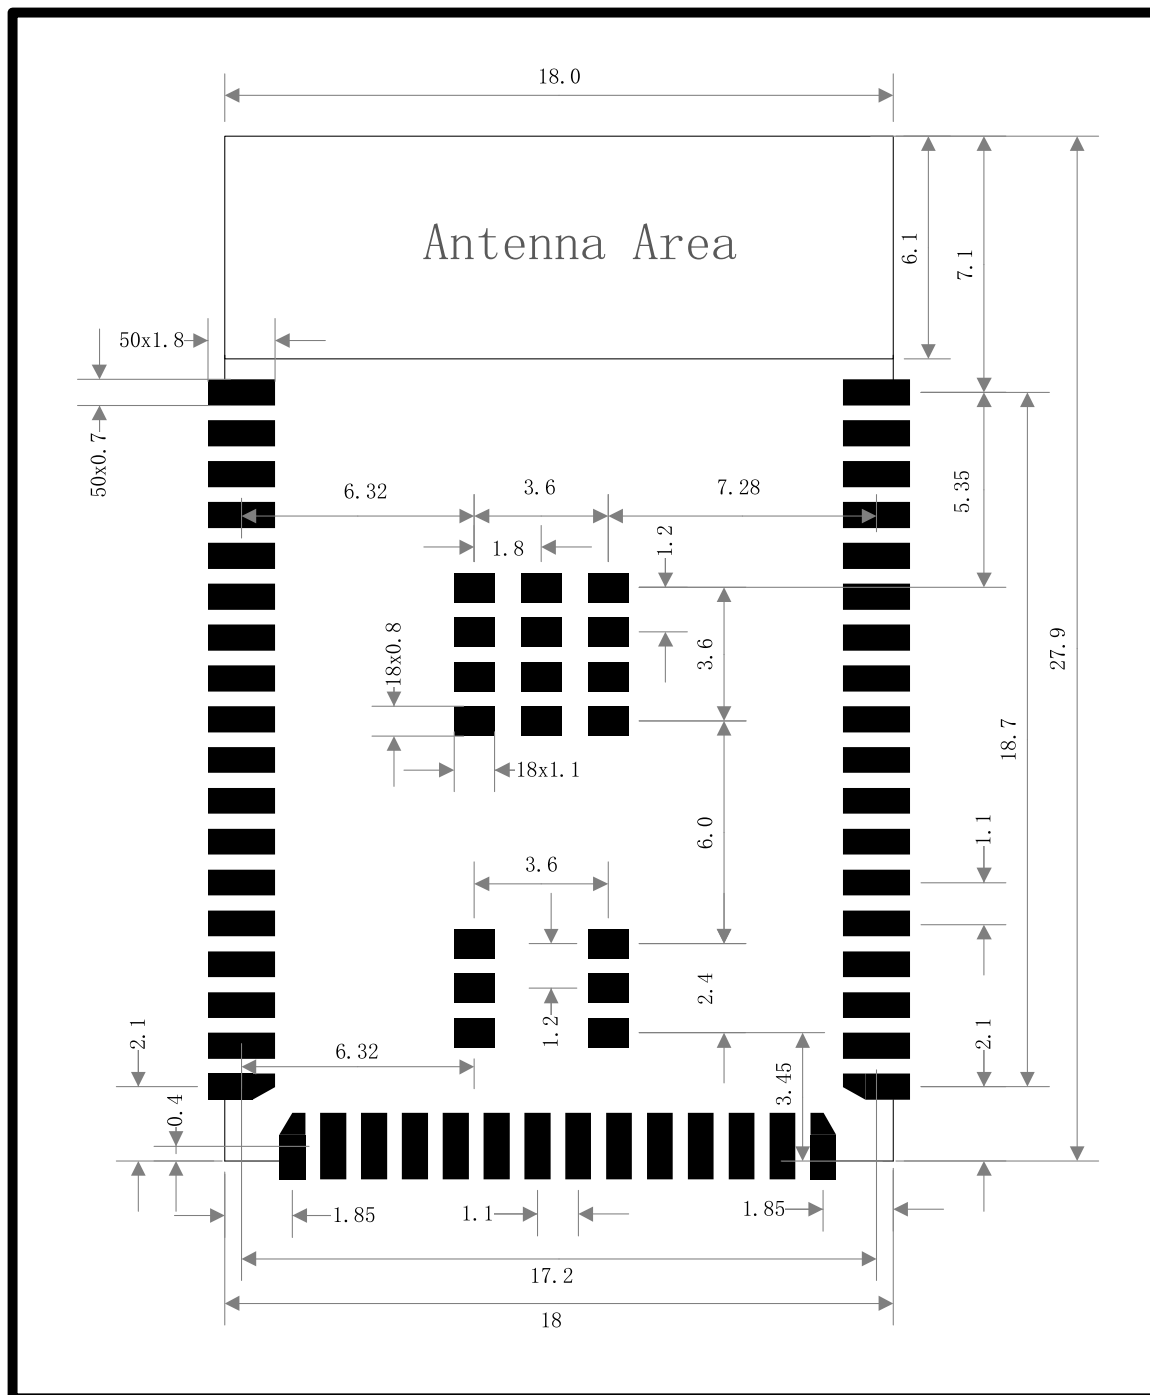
SF32LB52-MOD-1 推荐 PCB 封装图
